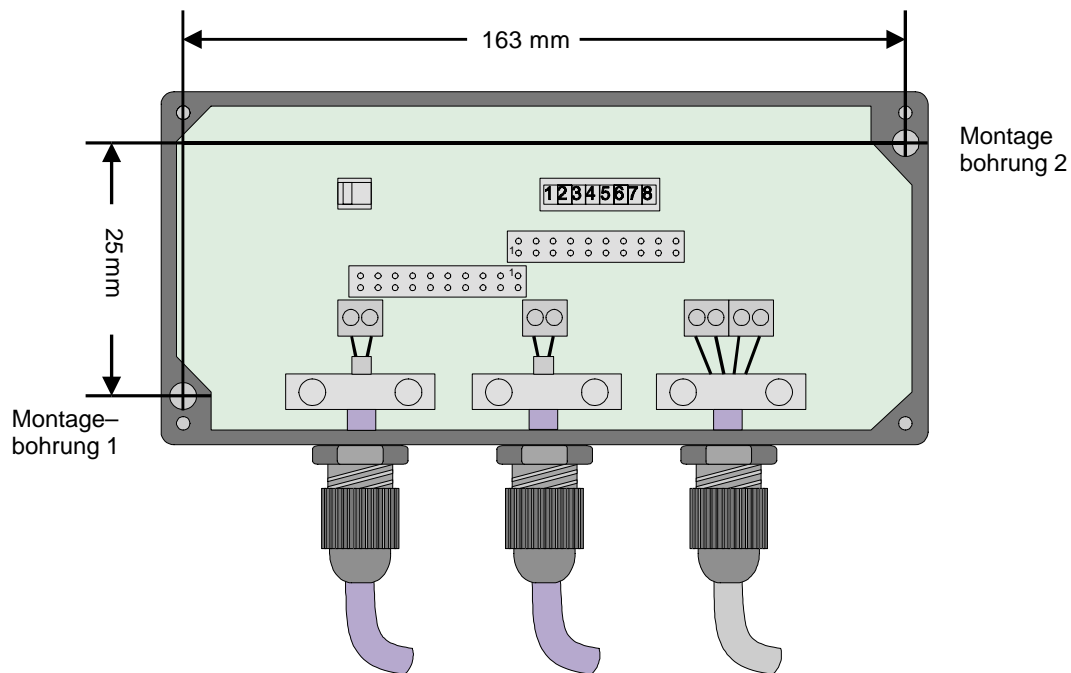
Bohrungsbezeichnung zur Befestigung des PROFIBUS ILM auf einer Montageplatte
